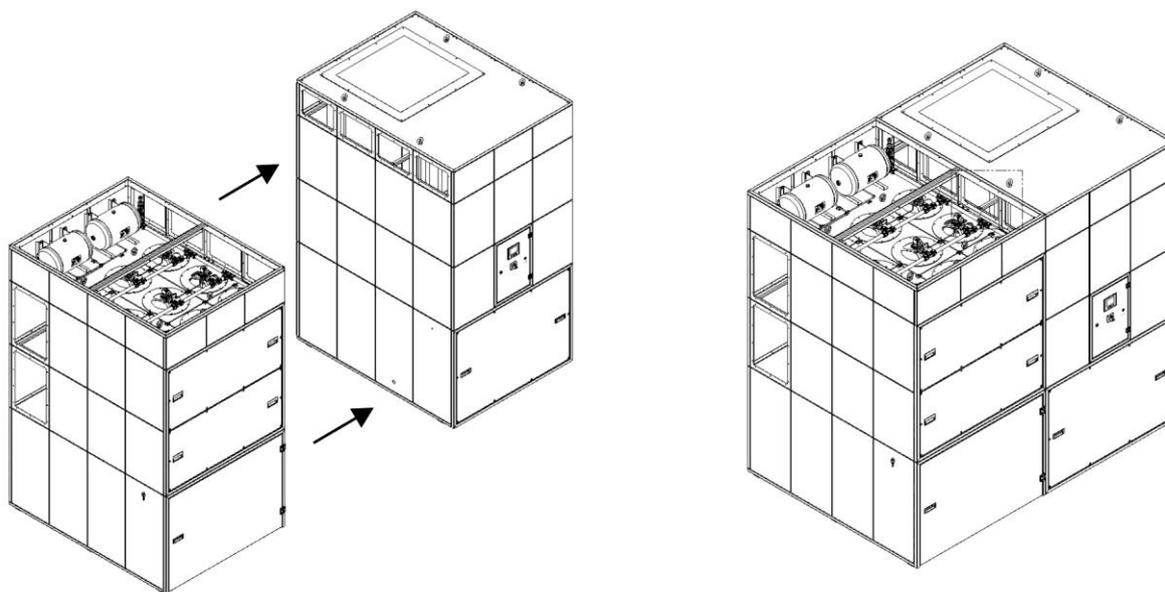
raccordement de la section du filtre à la section du ventilateur
